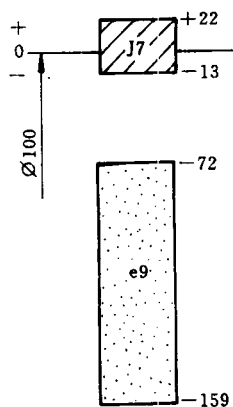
箱体孔与端盖定位圆柱面的公差带示意图
